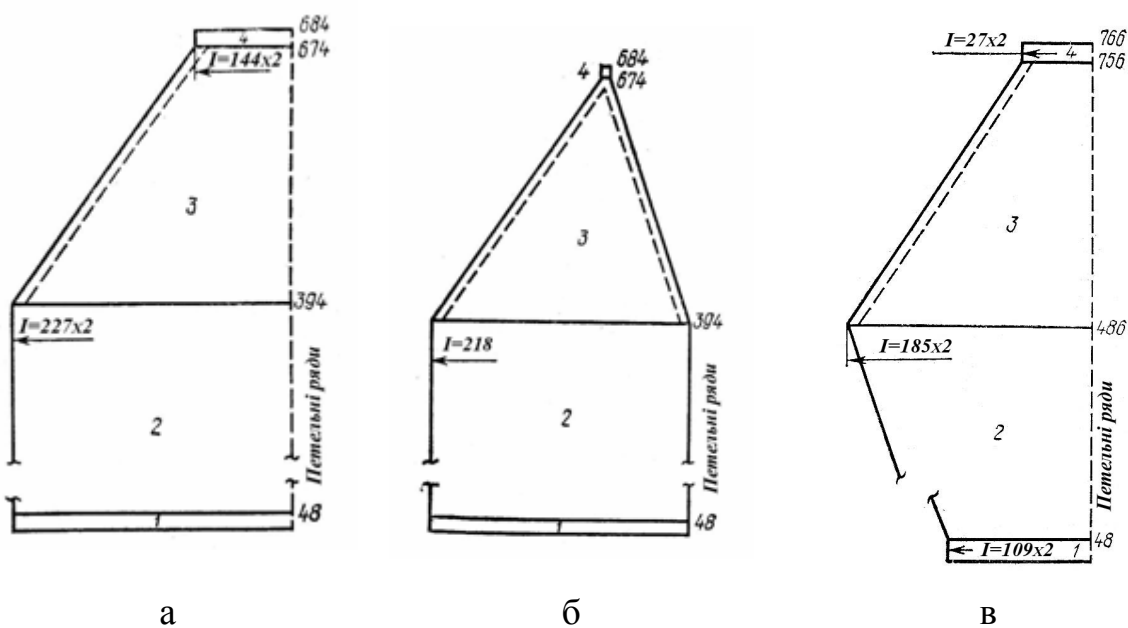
Робоче креслення деталей жакету: а – спинки; б – пілочки; в – рукава
